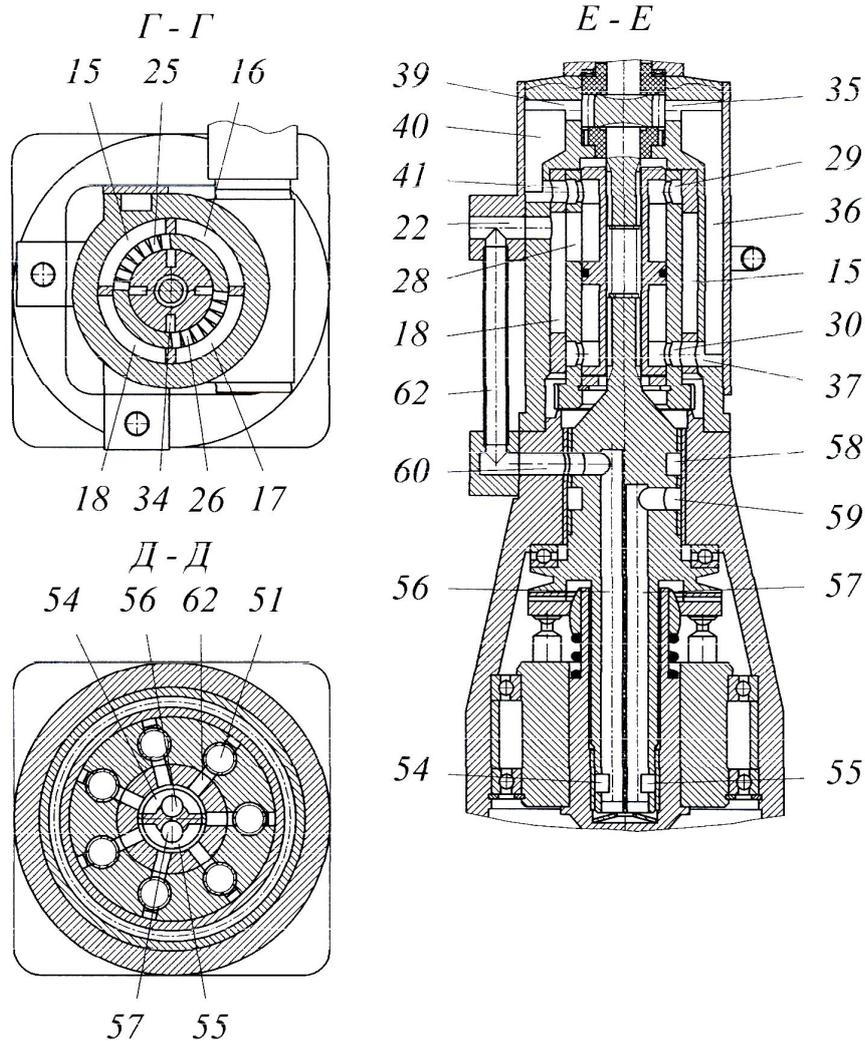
(продолжение). ОГП с планетарным редуктором в линии связи блока цилиндров гидромотора и ведомого вала
